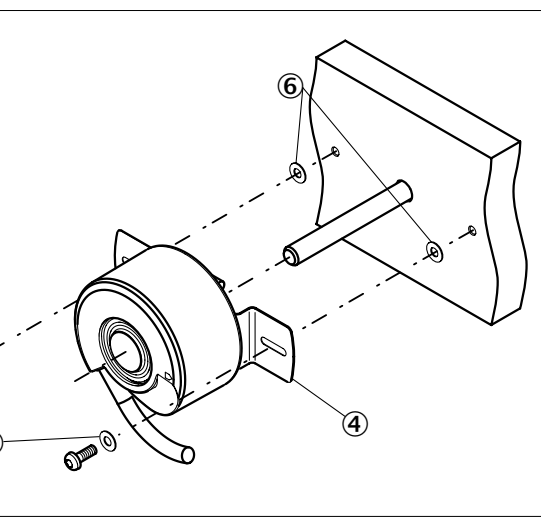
Anbau Servoflansch über flanschseitige Gewindebohrungen
